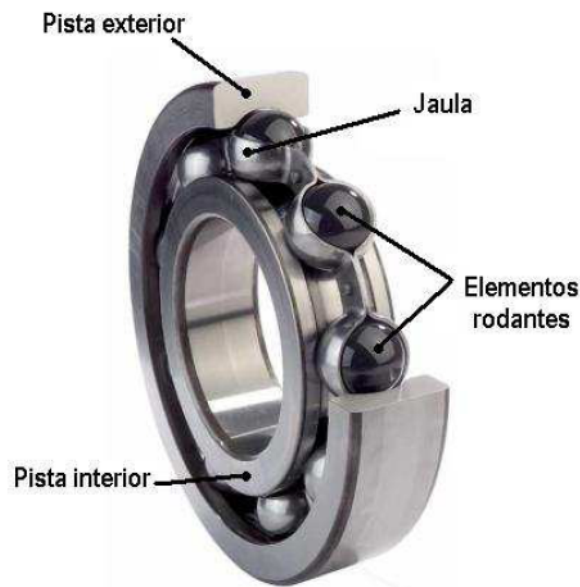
Partes fundamentales de un rodamiento de bolas.
